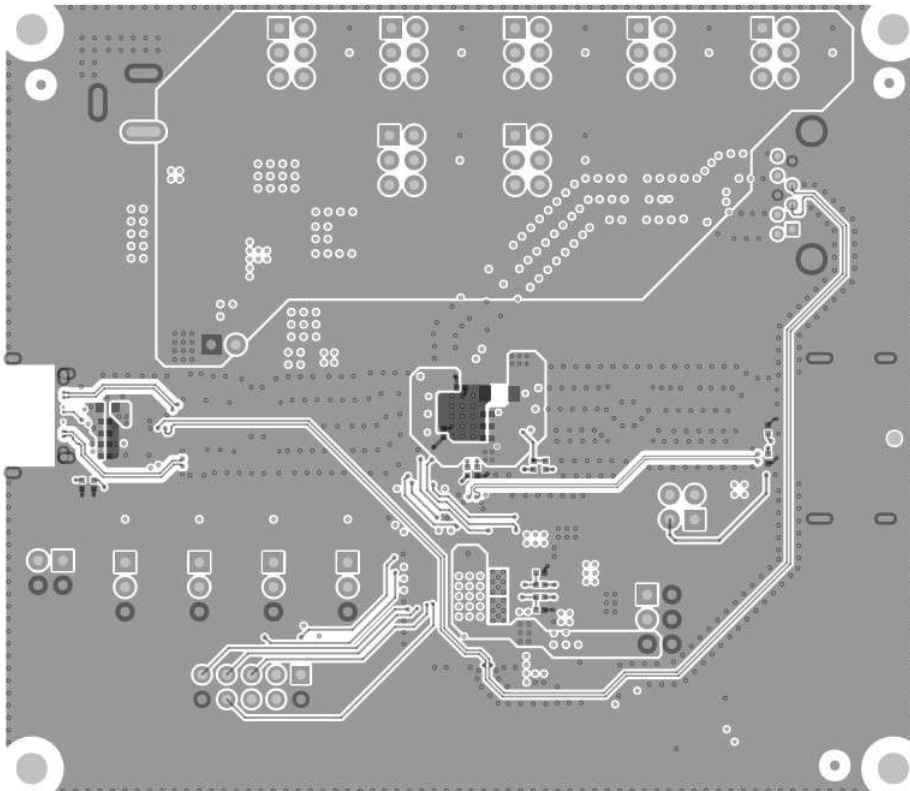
TUSB564-Q1 EVM PCB 第 6 层 (底部)
